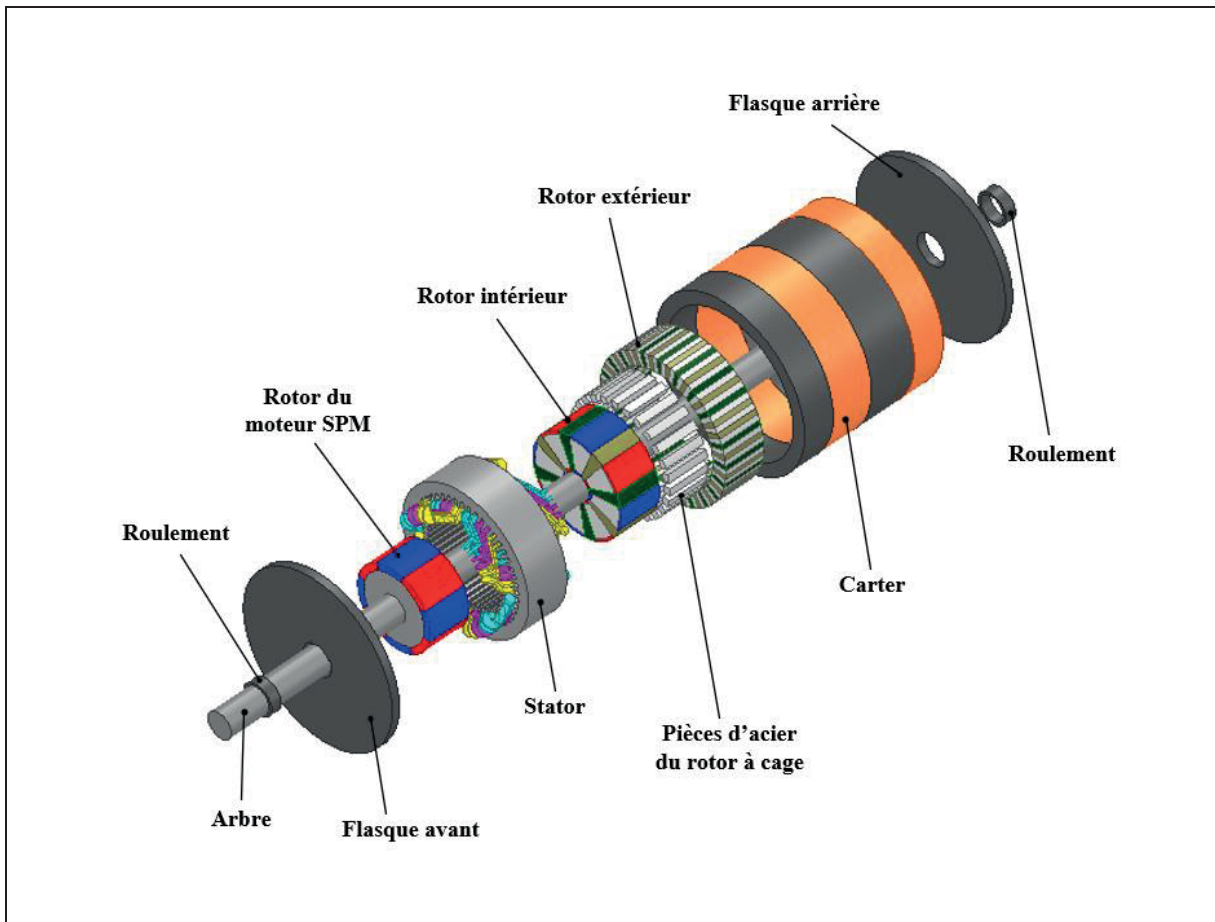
Vue en éclaté de la machine à engrenage magnétique proposée
